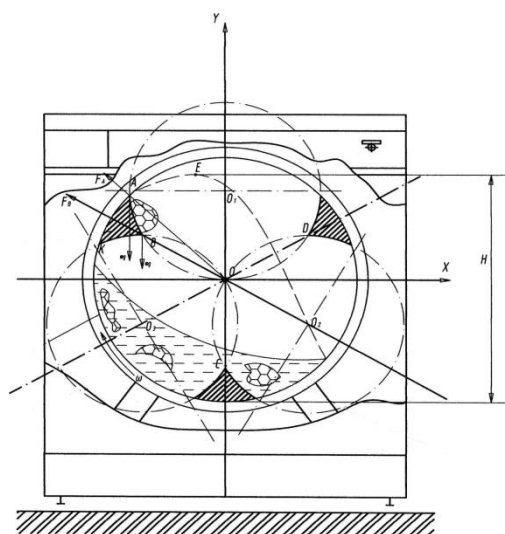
Загальний вид пральної машини й обичайки барабана з закріпленими гребенями(поперечний переріз)
